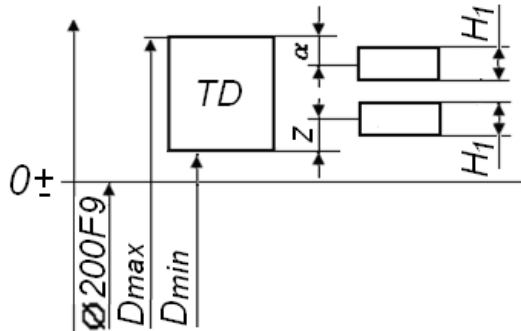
Схема розташування полів допусків калібра-пробки
